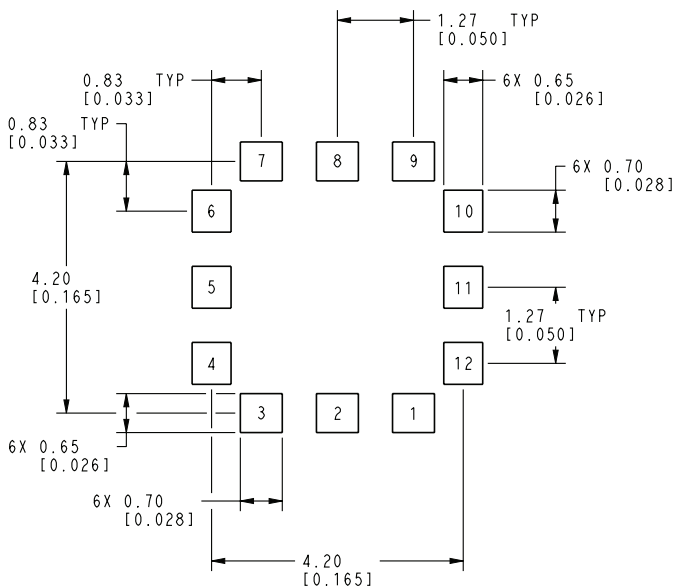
ロングポートセンサーと推奨 PCB パッドレイアウトの寸法 (参考のみ: MM [IN])
